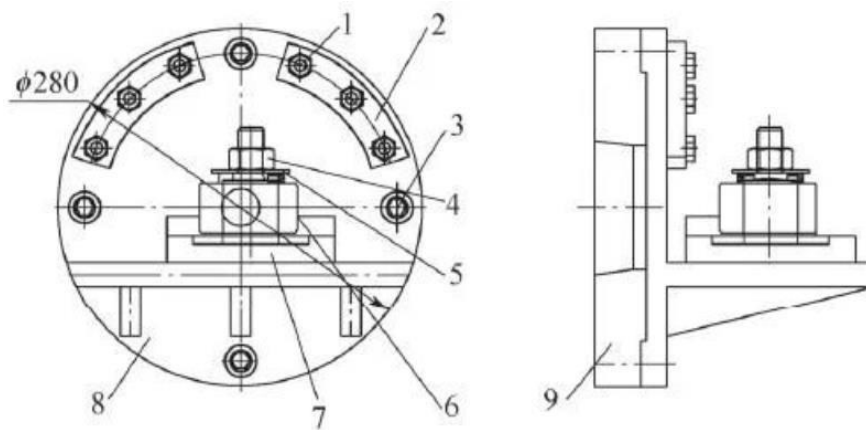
Разработка и сборка приспособления для обработки эксцентриковых отверстий в верхней торцевой крышке корпуса
